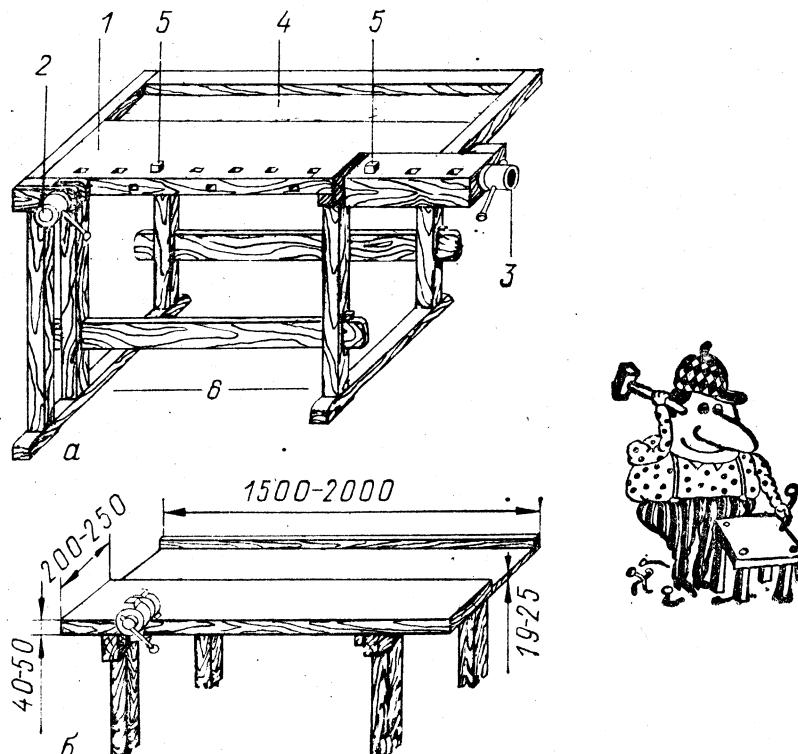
Верстак [а] и верстачная доска со съемными тисками [б]: 1 — верстачная доска; 2 — передние тиски; 3 — задние тиски с коробкой; 4 — лоток; 5 — клиновой упор; 6 — подверстачье
